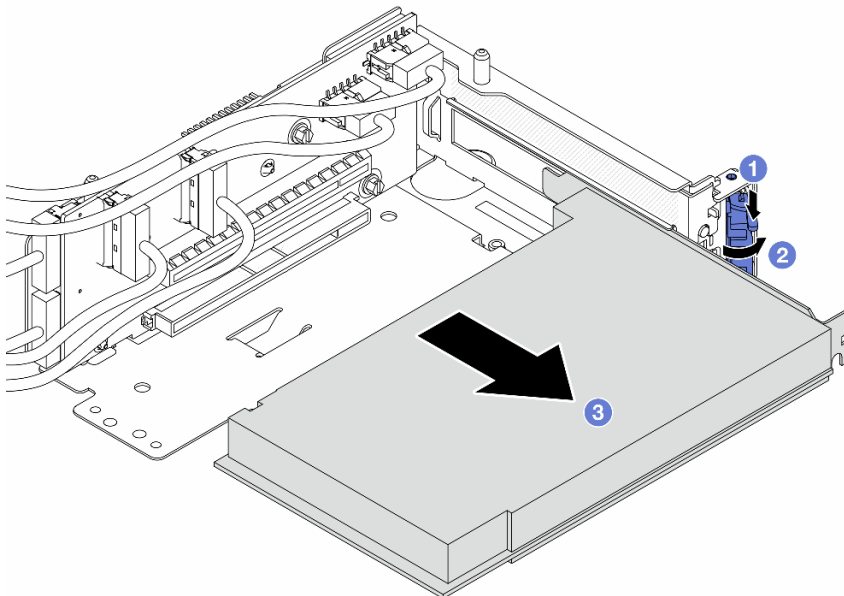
Entfernen des PCIe-Adapters von Adapterrahmen 5
